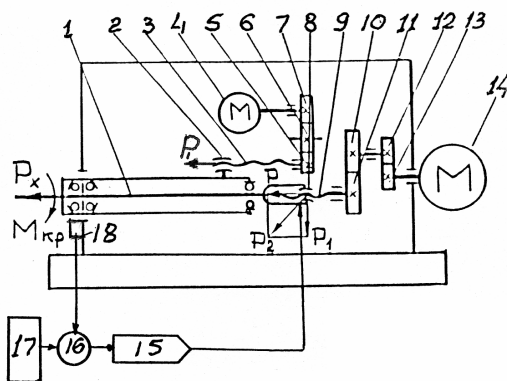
Кінематична схема силової головки агрегатного верстата
